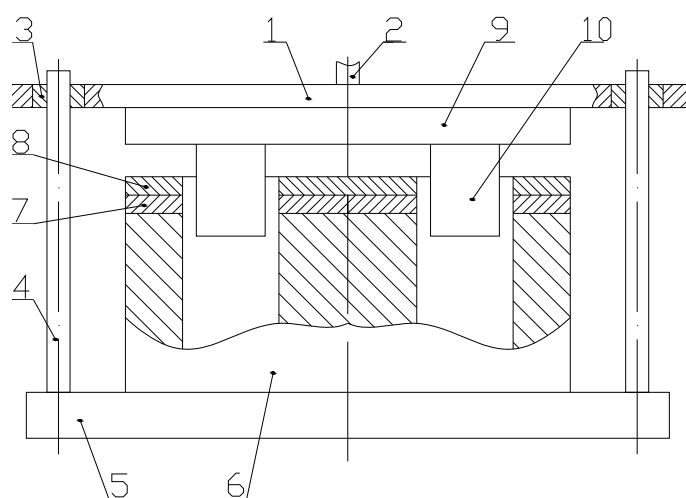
Принципиальная конструкция штампа для холодной штамповки
